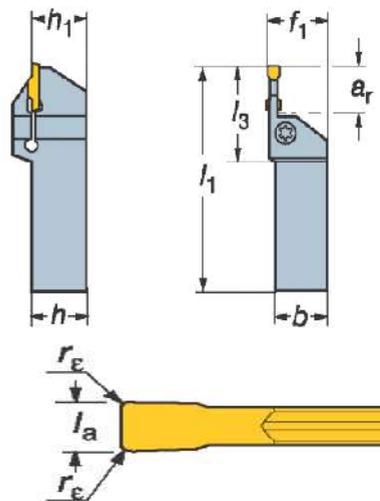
Типичная конструкция реза для отрезки и формирования канавки на наружной цилиндрической поверхности
